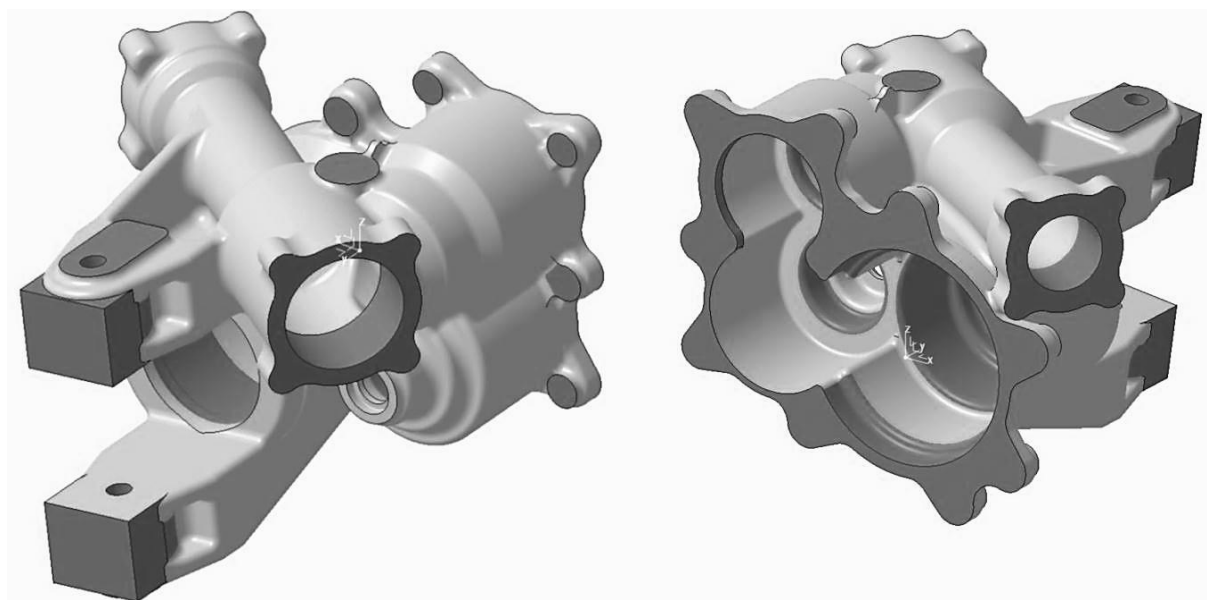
Общий вид оптимизированной литейной заготовки для детали «корпус»
